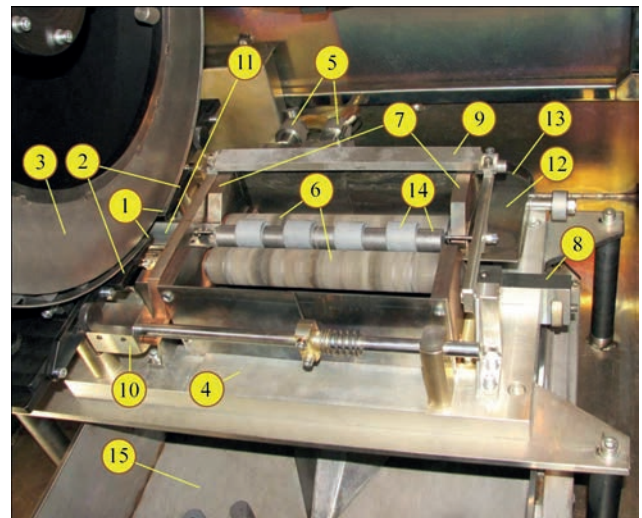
Внутрішньокамерне оснащення для ЕПО крупним планом: деталі барабанного магазину: 1 – щілина у зовнішній обичайці; 2 – пара нижніх повздовжніх стулок; 3 – торцева кришка барабана; деталі обертача: 4 – базова плита; 5 – водяне охолодження базової плити; 6 – робочі валки; 7 – пара опорних шік одного з валків; 8 – шаблон для позиціонування валків; 9 – підйомна рамка обмежувачів деталей; 10 – блокуючий кулачок фіксатора підйомної рамки; 11 – приймальний лоток; 12 – похилий вивантажувальний лоток; 13 – гвинтовий лоток; інше; 14 – заготовки та графітові проставки; 15 – піддон для оброблених деталей
